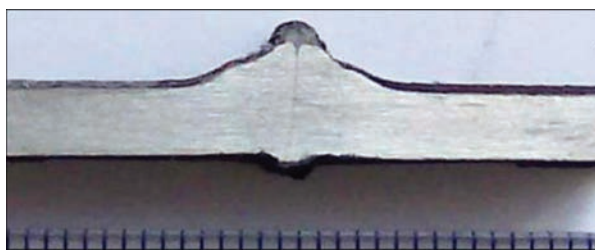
Макрошлиф сварного соединения трубы диаметром 42×3,5 мм
